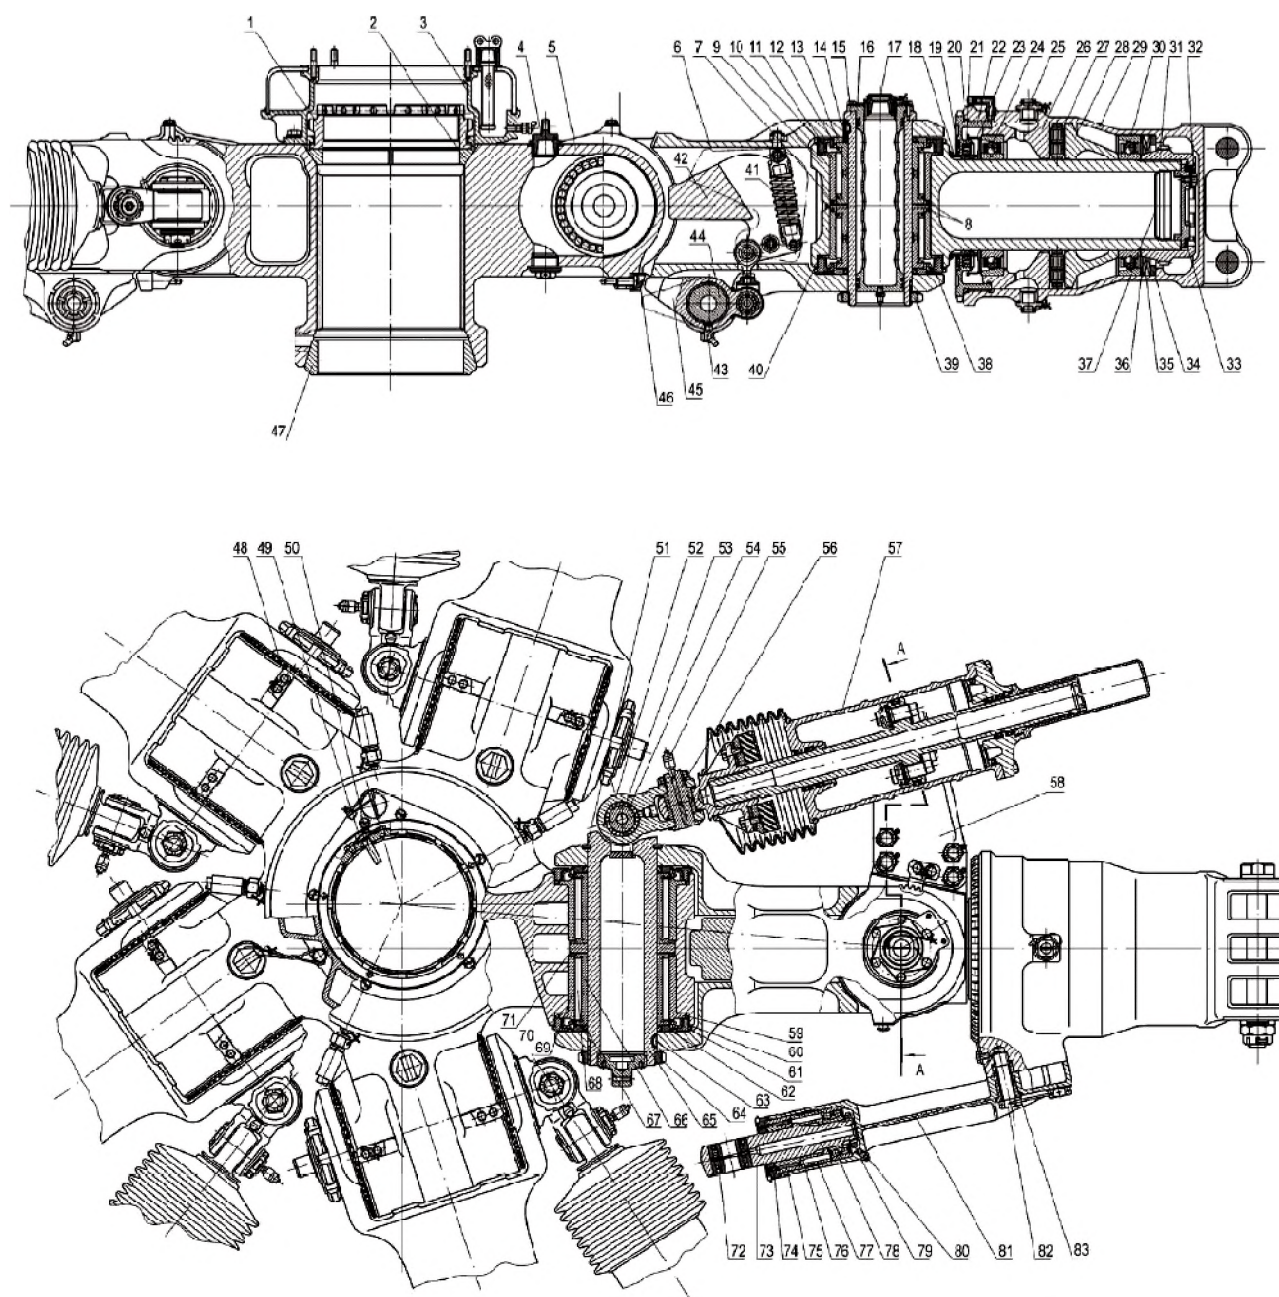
Конструкция шарнирной втулки НВ вертолета Ми-8 [8]:
